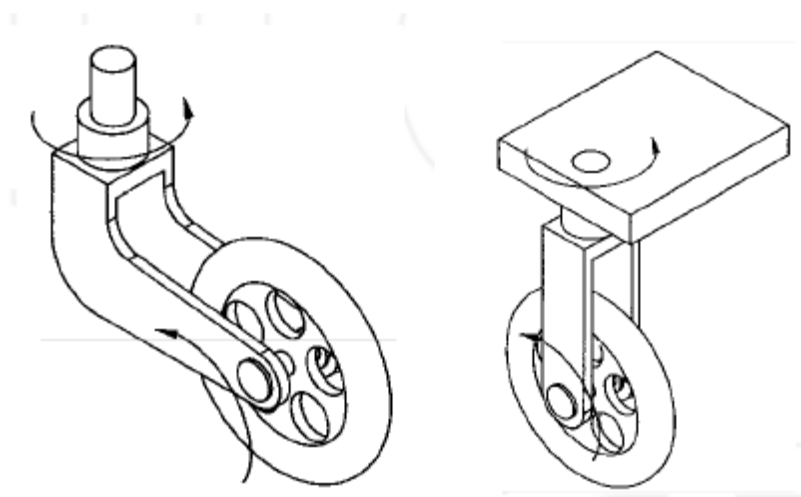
Roda direcional (direita) e roda rodízio (esquerda)
